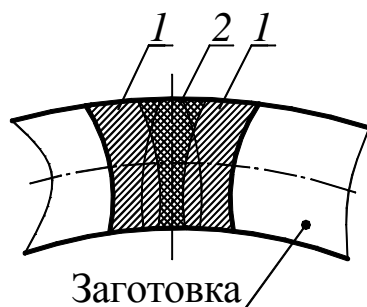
Схема получения выпуклых круговых зубьев при переменном расстоянии между осями заготовки и инструмента:
